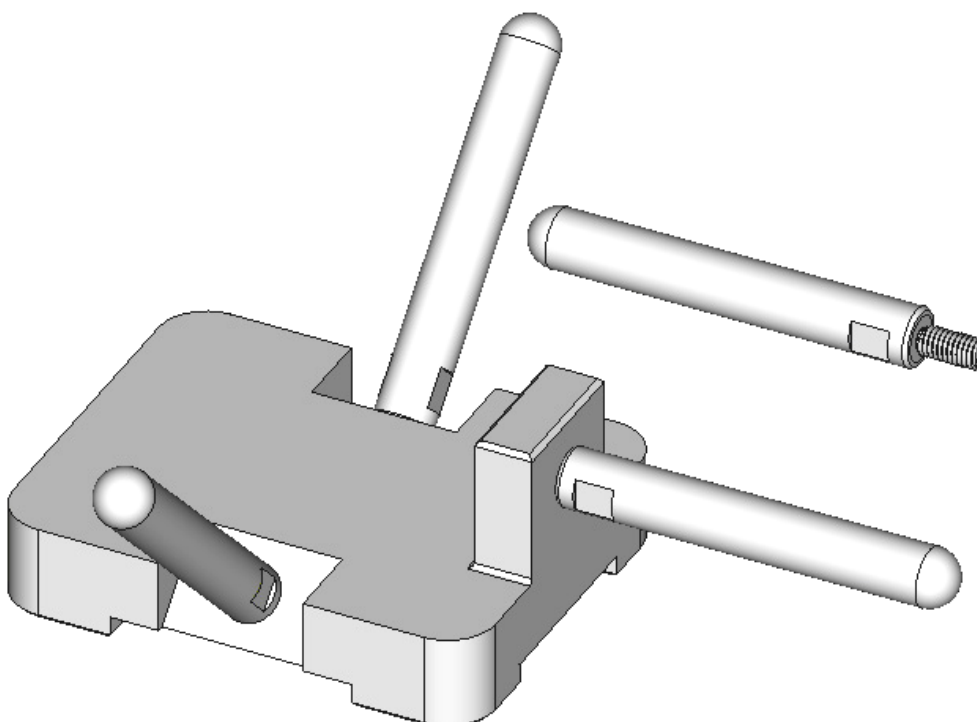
Рукоятка простая («винт»): заворачивается в корпус
